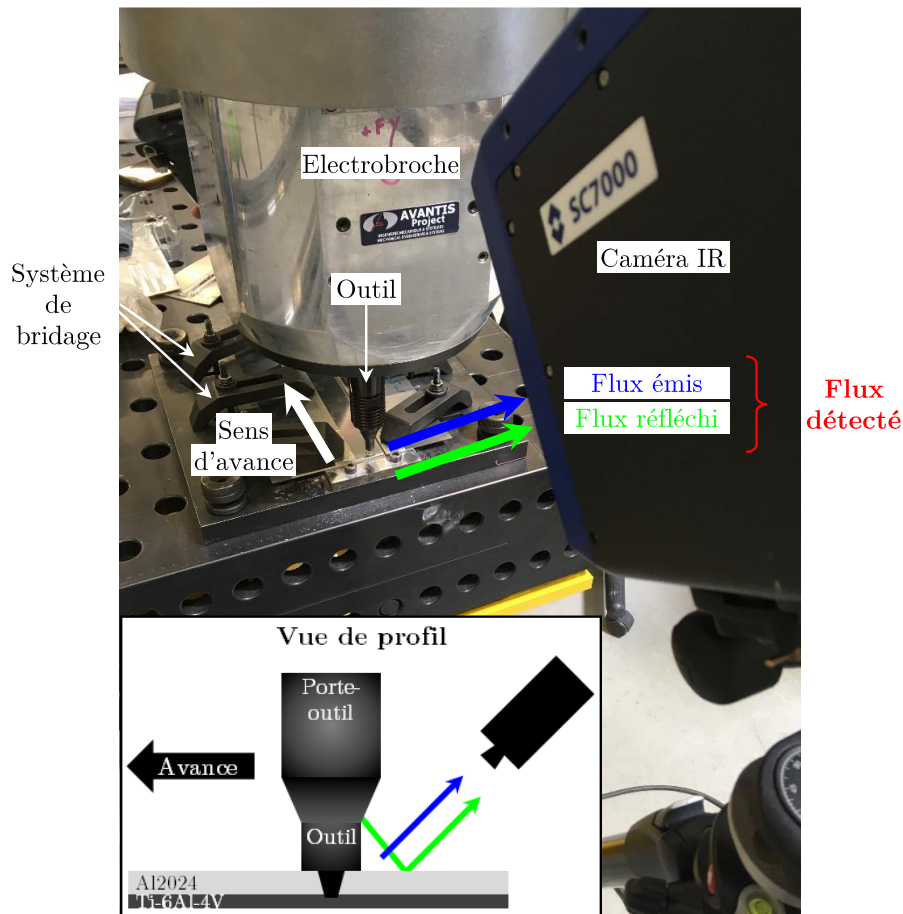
Dispositif expérimental pour l'instrumentation des essais de soudage par thermographie IR.
